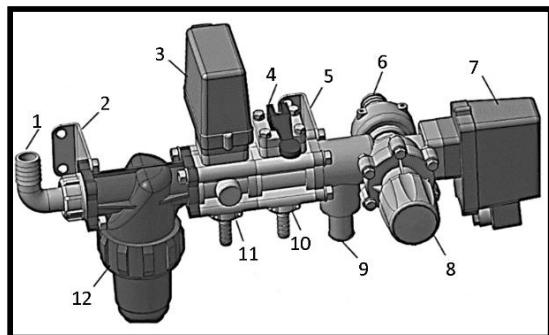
Общий вид регулятора давления: 1 – главный
